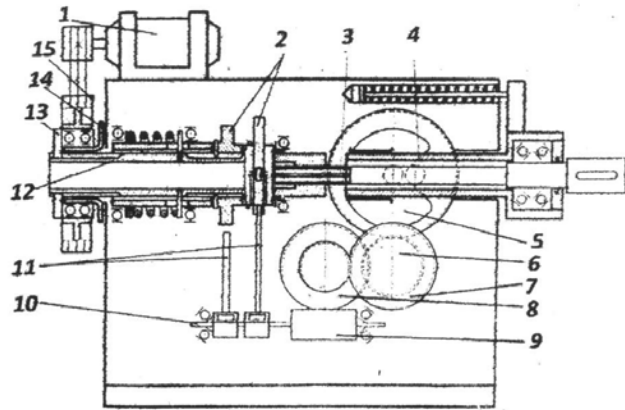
Передаточний механізм силової головки агрегатного верстата
